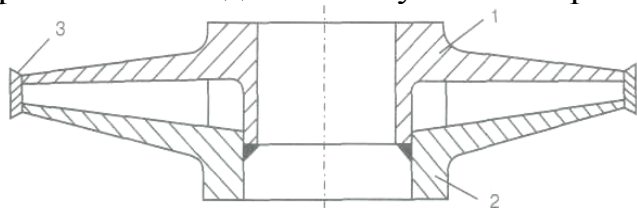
Схема твердого кріплення дисків колеса зварюванням: 1 – основний диск; 2 – зварений шов у маточині; 3 – бандажні стяжки
